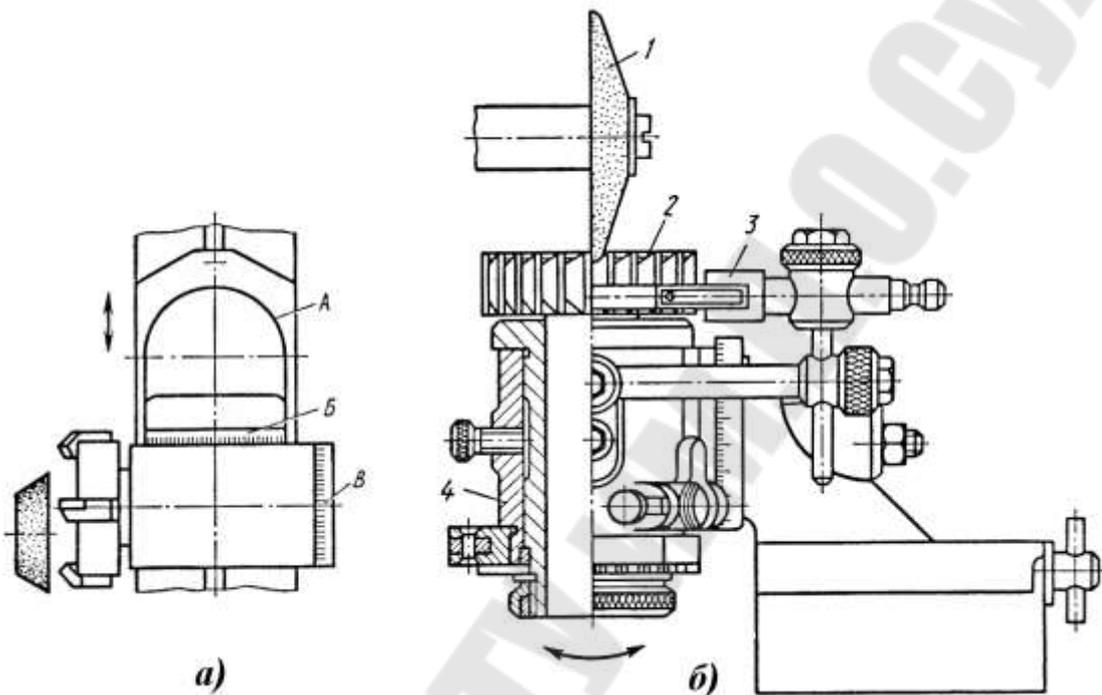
Исходное положение большой универсальной головки перед заточкой задних поверхностей торцовой фрезы (а), схема заточки передней поверхности торцового зуба трёхсторонней пазовой фрезы в малой универсальной головке: 1 – круг; 2 – фреза; 3 – упорка; 4 – головка.
